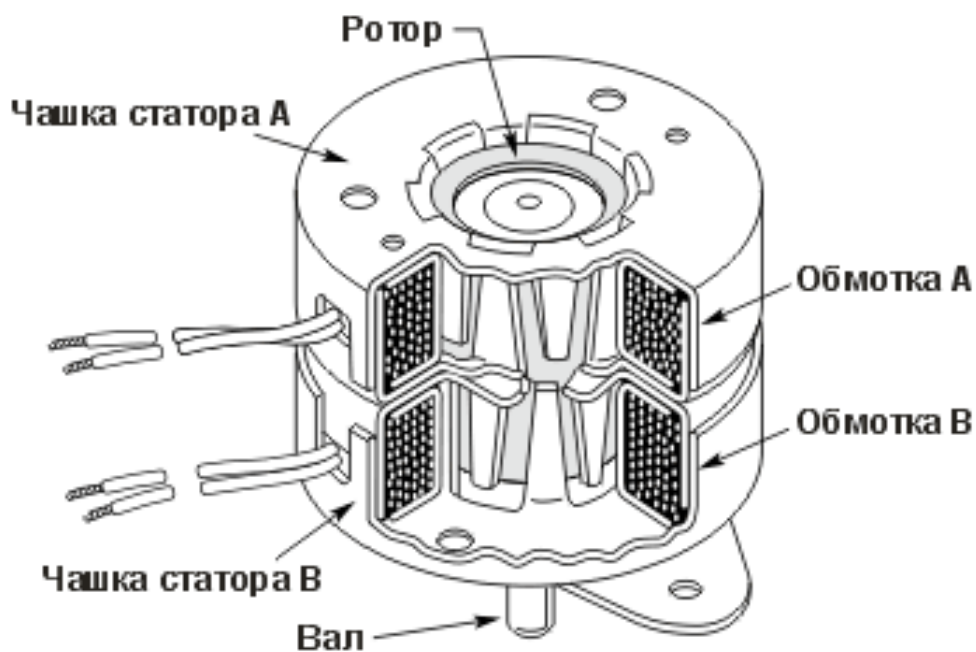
Разрез шагового двигателя с постоянными магнитами.
